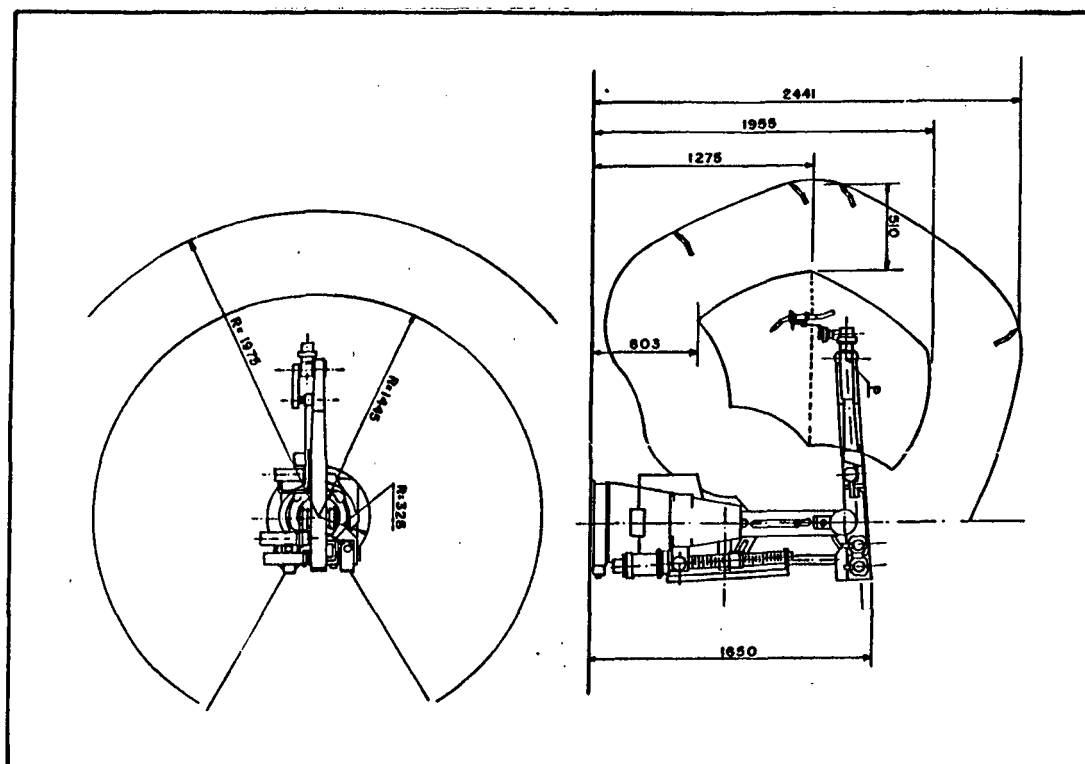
Domínio de liberdade da pistola de soldagem.
